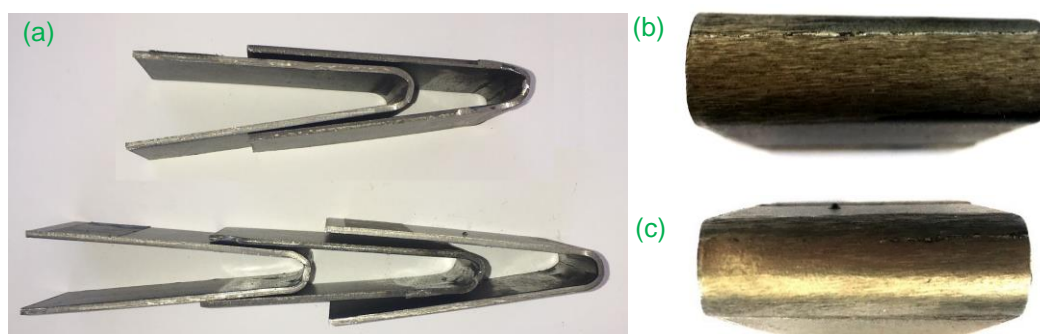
Ensaio de dobramento das chapas soldadas: (a) posição final de dobramento das chapas; (b) corpo de prova de baixa energia de soldagem; (c) corpo de prova de alta energia de soldagem.
